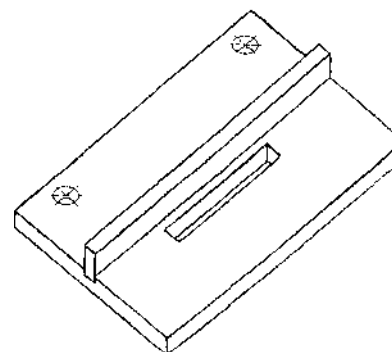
Загальний вигляд пристосування до верстата ФІШІ 5М для виготовлення ящиківих шипівих з'єднань
